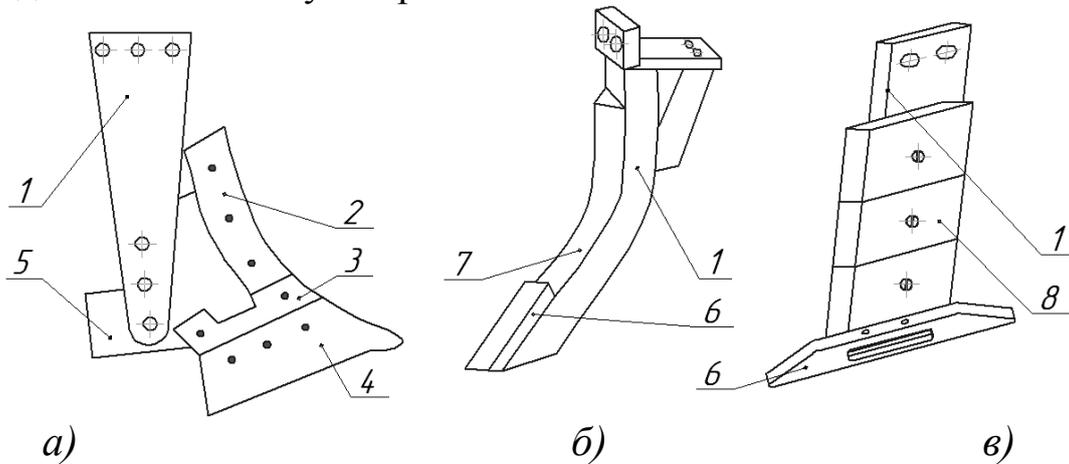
Формы рабочих поверхностей отечественных плужных корпусов
